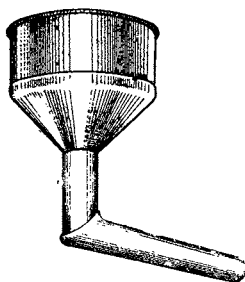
Воронка 240-85-сб. 111 для заливки масла в планетарный механизм поворота
